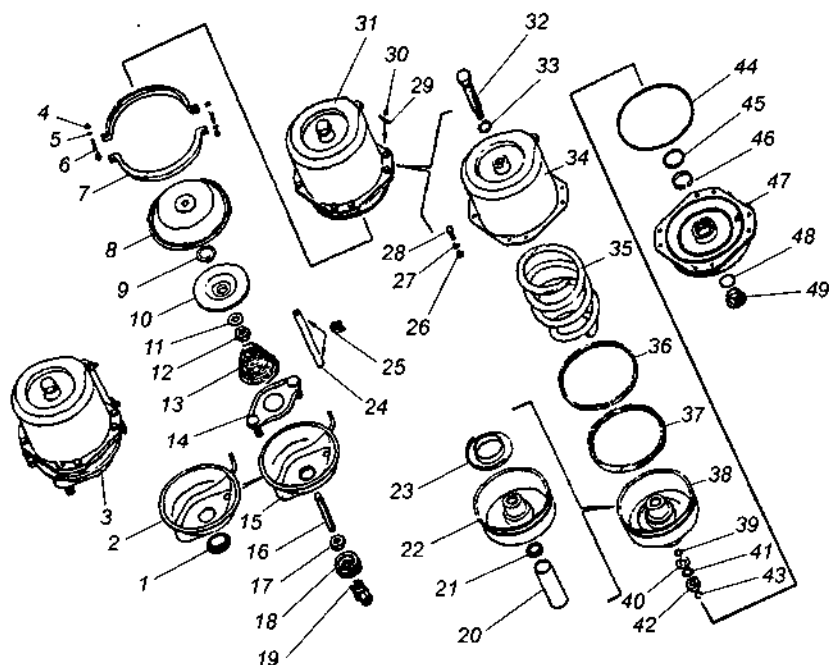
Тормозная камера типа 24×24 с пружинным энергоаккумулятором: 1 — фиксатор; 2 — корпус; 3 — тормозная камера с пружинным энергоаккумулятором; 4, 12, 17, 26 — гайки; 5, 27 — пружинные шайбы; 6, 28 — болты; 7 — хомут; 8 — мембрана; 9 — колпачок; 10 — диск; 11, 21 — плоские шайбы; 13, 35 — пружины; 14 — фланец; 15 — корпус; 16 — шток; 18 — защитный чехол; 19 — вилка; 20 — труба; 22, 38 — поршни; 23 — тарелка пружины; 24 — шланг; 25 — хомут; 29 — табличка; 30 — пустотелая заклепка; 31 — энергоаккумулятор; 32 — винт; 33 — уплотнительная шайба; 34 — цилиндр; 36, 46 — направляющие кольца; 37 — уплотнитель; 39, 44, 45, 48 — кольца; 40 — кольцо подшипника; 41 — подшипник; 42, 43 — упорные кольца; 47 — фланец; 49 — толкатель
